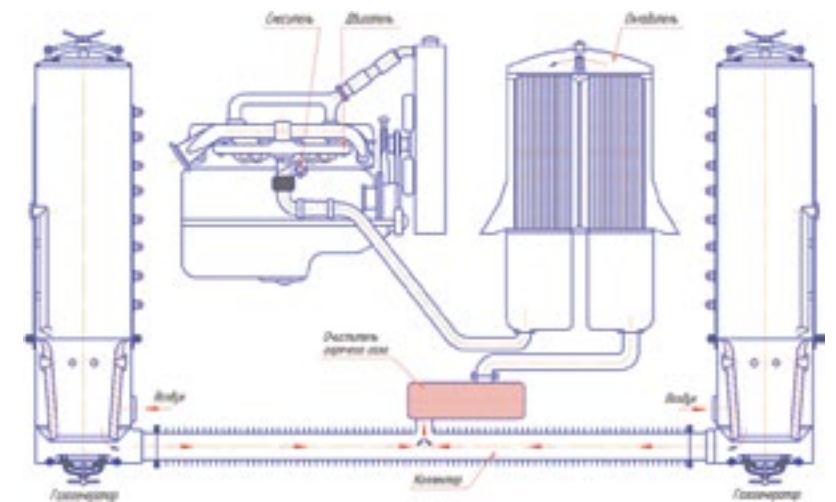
Схема газогенераторной установки конструкции В. П. Карпова
